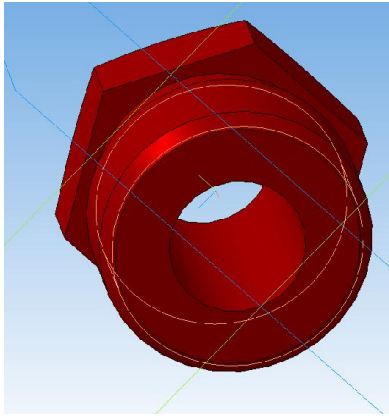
Гидро аппарат крановый, детализовка 3D сборки
